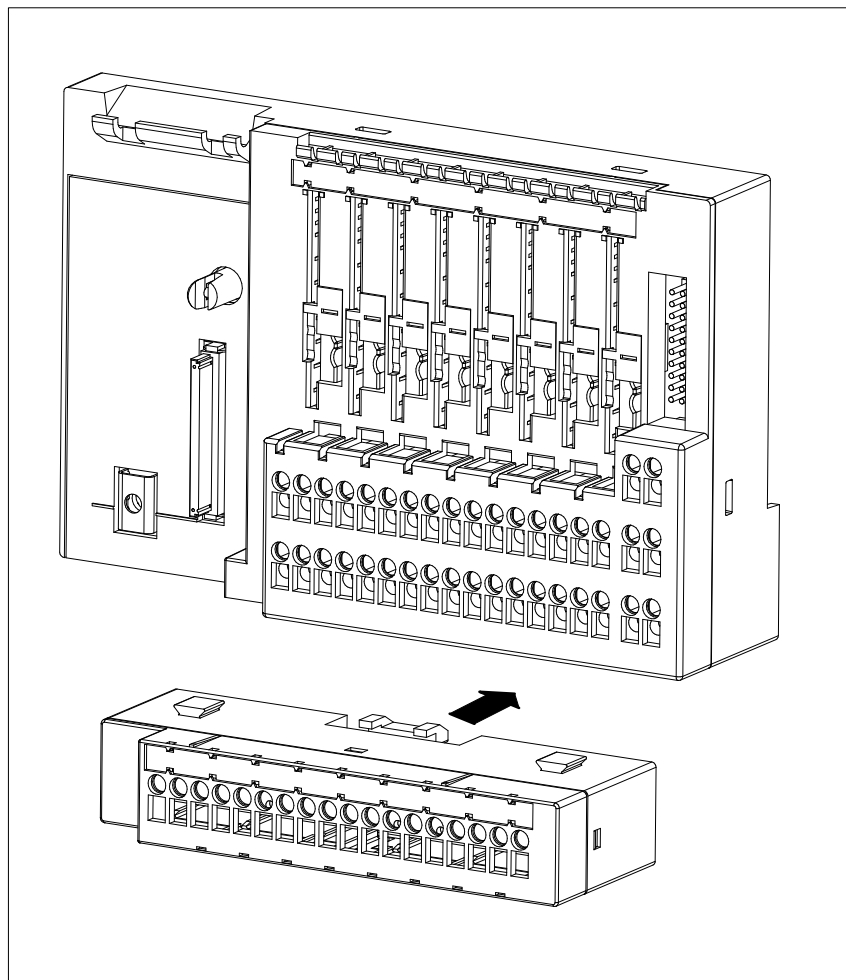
Zusatzklemme an Terminalblock befestigen
